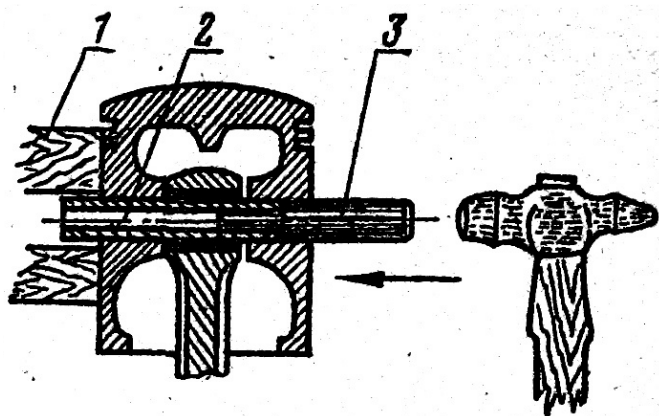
Снятие (и установка) поршневого пальца: 1 — деревянный брус; 2 — палец; 3 — оправка
